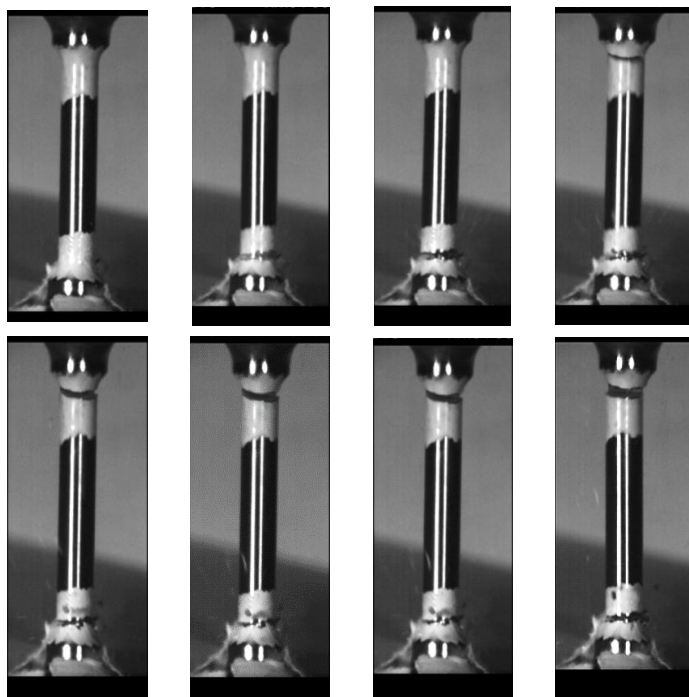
Кадры скоростной съемки, фиксирующие процесс двойного разрушения образца шарикоподшипниковой стали
